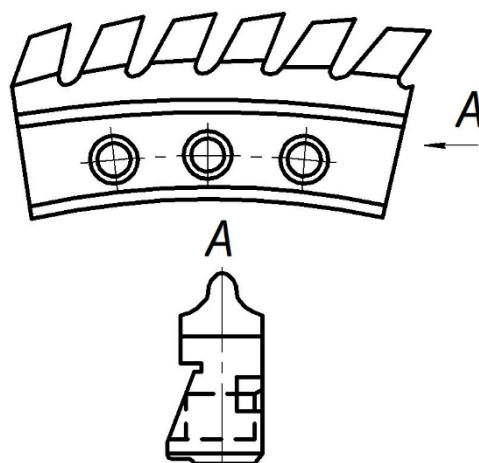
Схема блочного різця на головці для кругового протягування
